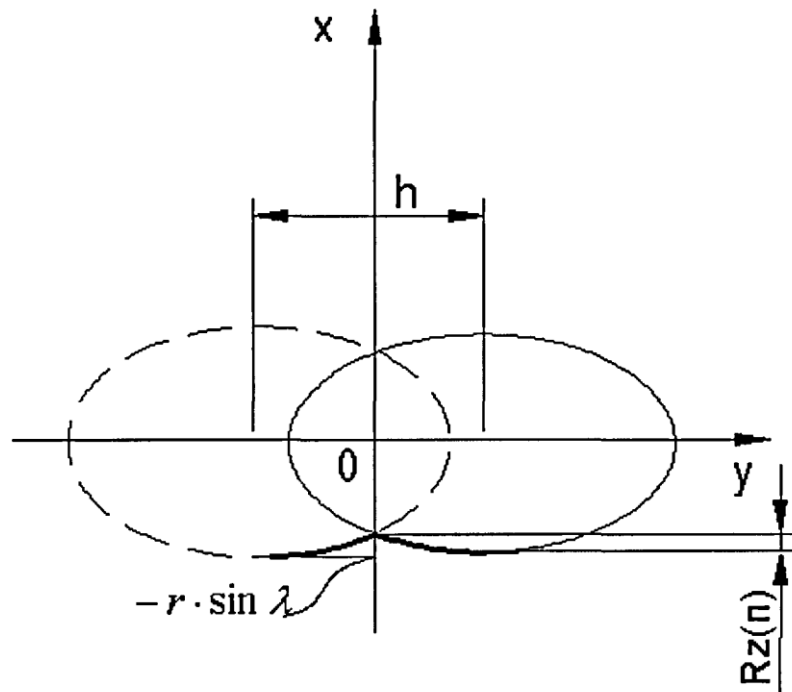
Схема к расчету «поперечной» шероховатости при фрезеровании торoidalной фрезой
